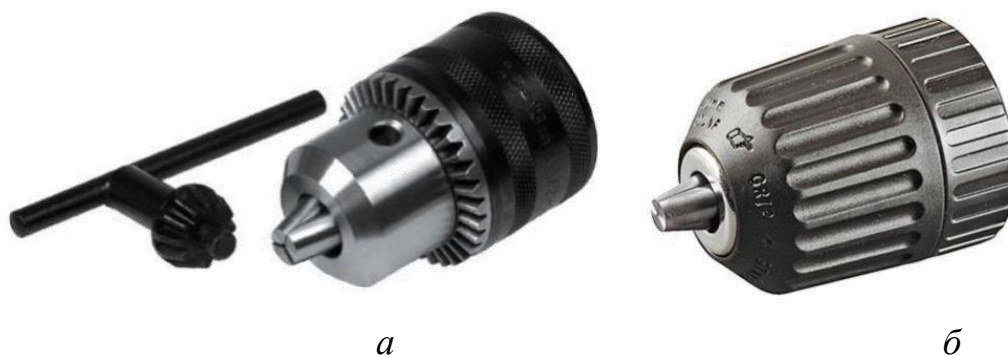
Патрони для закріплення свердильного інструменту: а – патрон ключовий, б – патрон швидкозатискний
